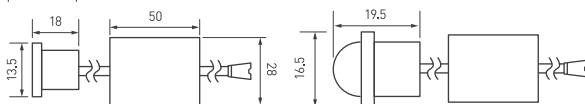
Габаритные размеры датчика SR-PRIME-MINI
